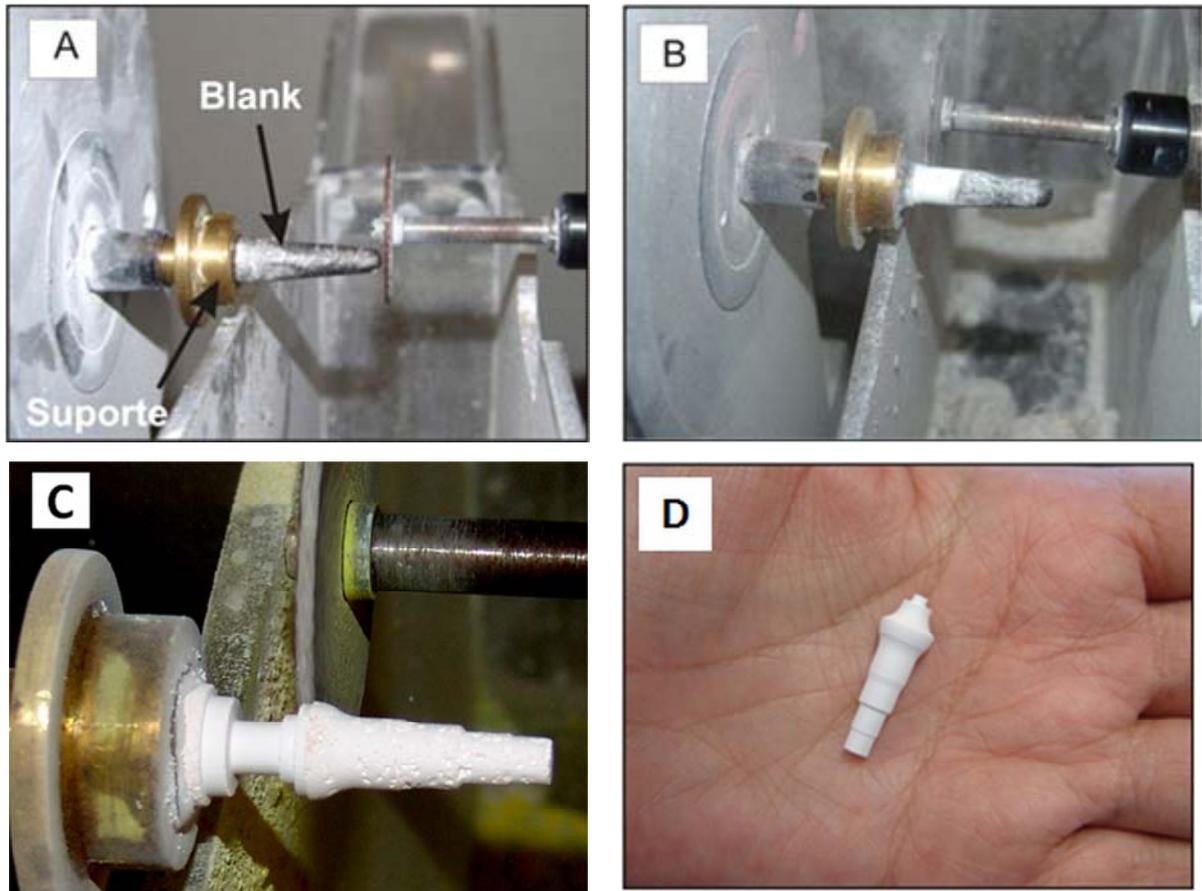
Usinagem de *blank* no formato de pino de dente. (A) *Blank* fixado no suporte. (B) *Blank* durante usinagem. (C) Usinagem em fase final de acabamento. (D) Pino usinado.
